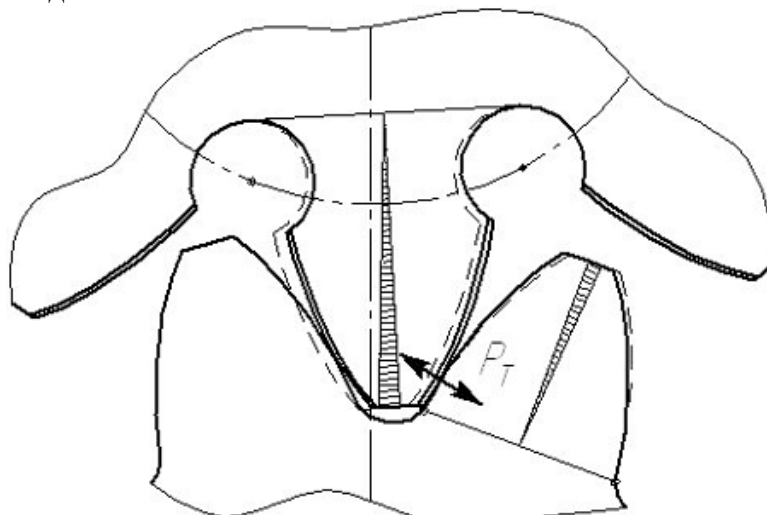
Эпюры изгибов зубьев шеввера и обрабатываемого колеса под действием тангенциальной силы
